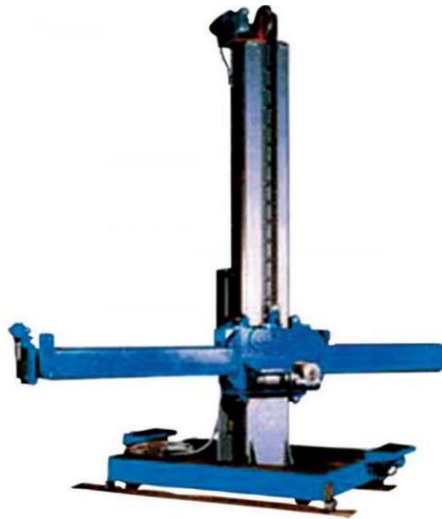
Загальний вигляд зварювальної колони BCZQ 2x2
